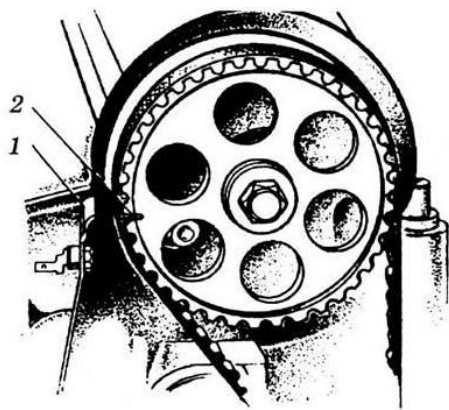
Проверка совпадения меток на звездочке распределительного вала и корпусе подшипников:
